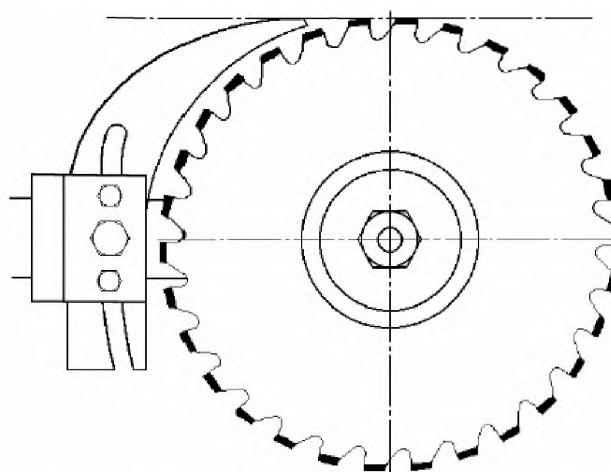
Вертикальная установка расклинивающего ножа относительно дисковой пилы
